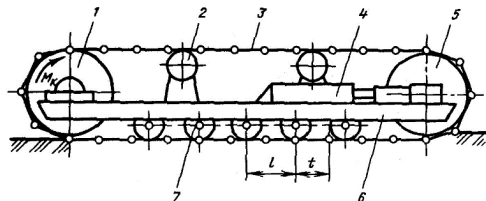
Многоопорный гусеничный движитель с жесткой подвеской опорных катков
